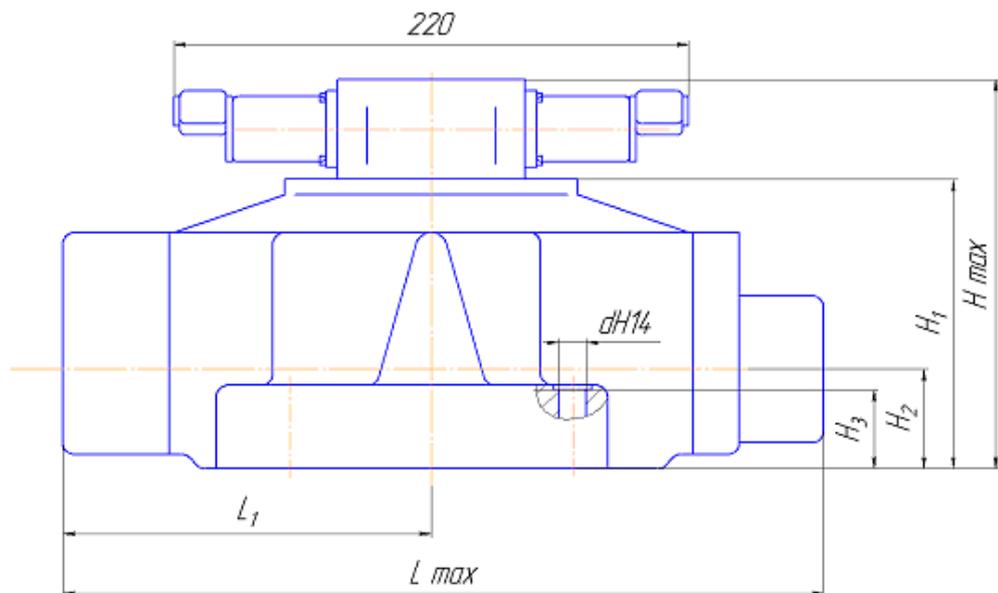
Габаритные и присоединительные размеры присоединительных плит.
